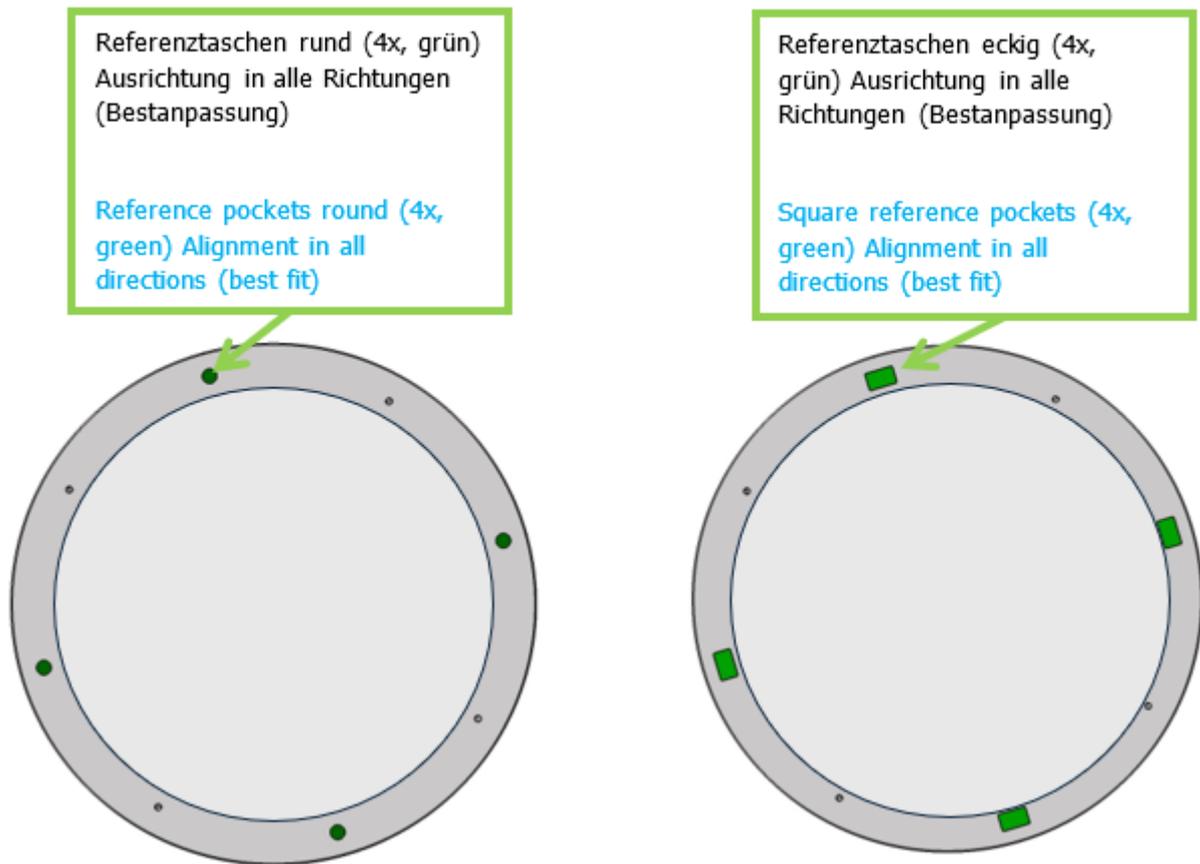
Ausrichtung für Werkzeuge, Formen und Vorrichtungen
